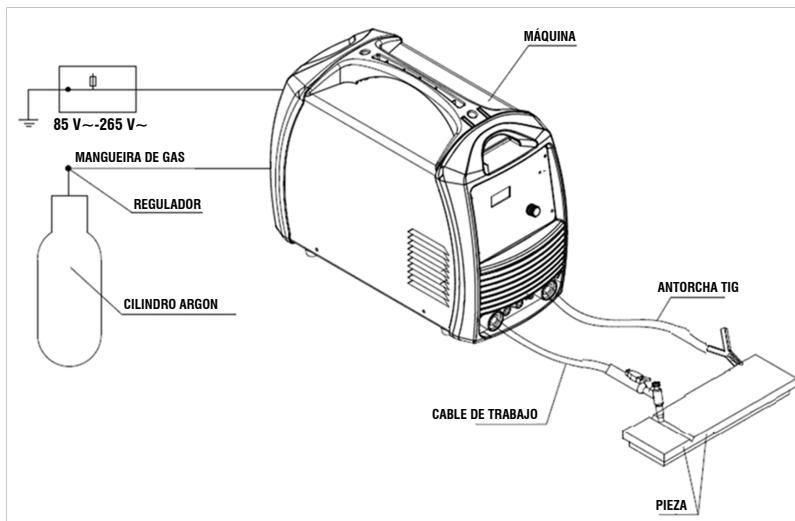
Montaje del conjunto de soldadura TIG
